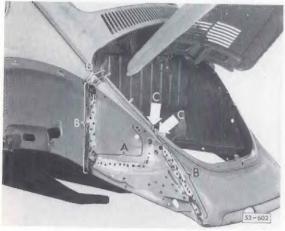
Seitenteil-Auschnittsteil, Motorabdeckblech und Auschlußblech hinten einschweißen.
